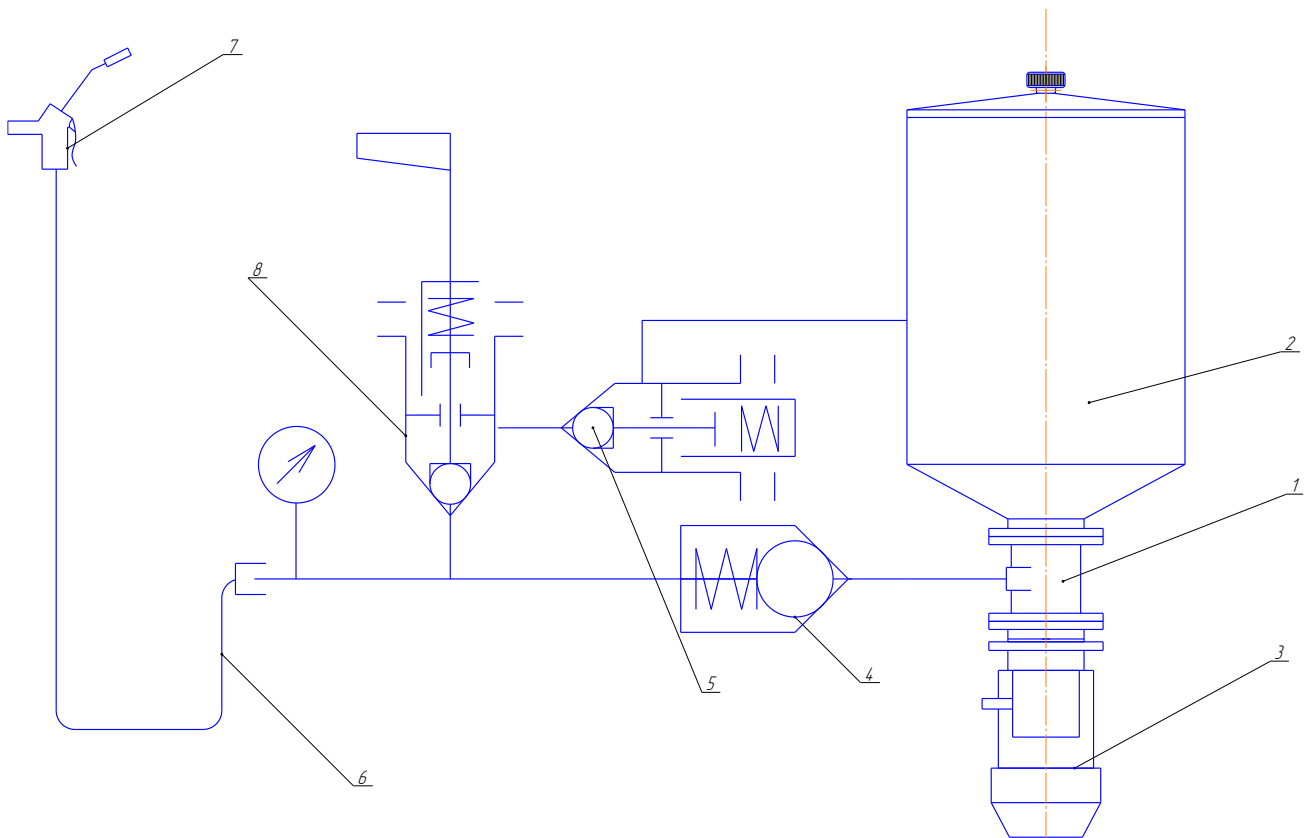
Принципова схема пристосування для заправки змазкою:
